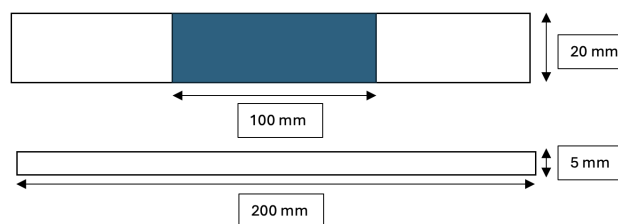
Dimensi Spesimen Uji Tarik ISO 4136
